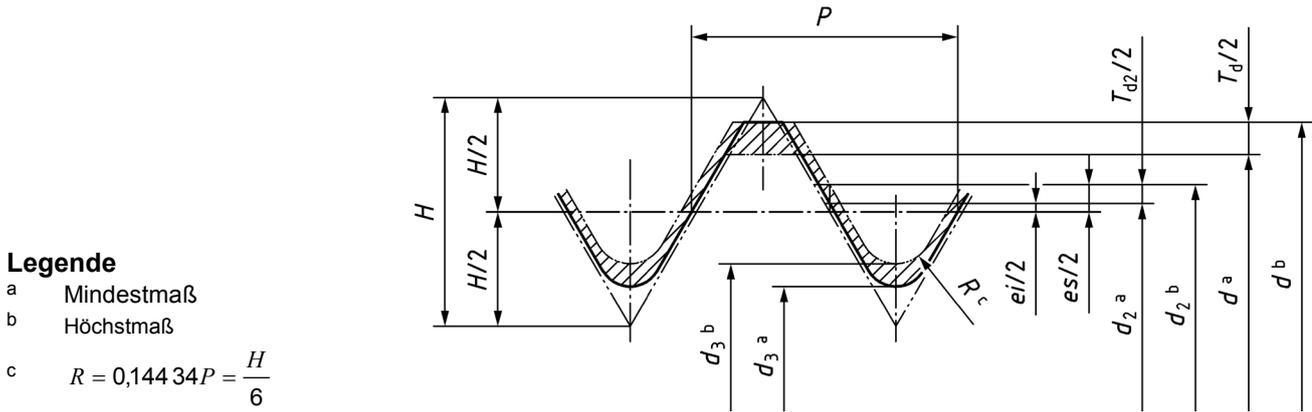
Außengewinde mit positivem Grundabmaß im Flankendurchmesser; Toleranzfeldlage Sn 4
